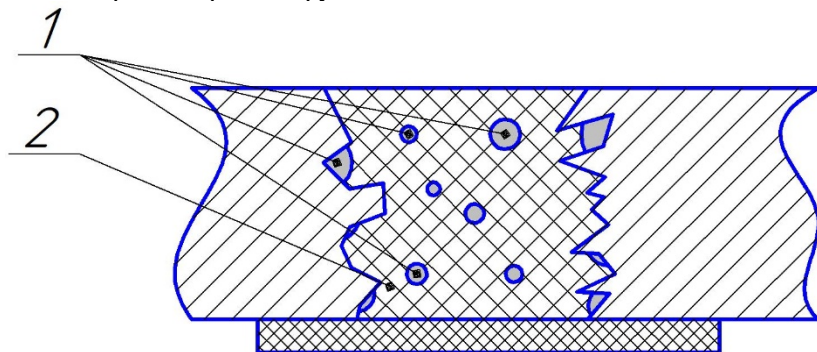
Газовая шероховатость металлополимера после отверждения. 1 – газовые поры и раковины; 2 – отвержденный металлополимер.
